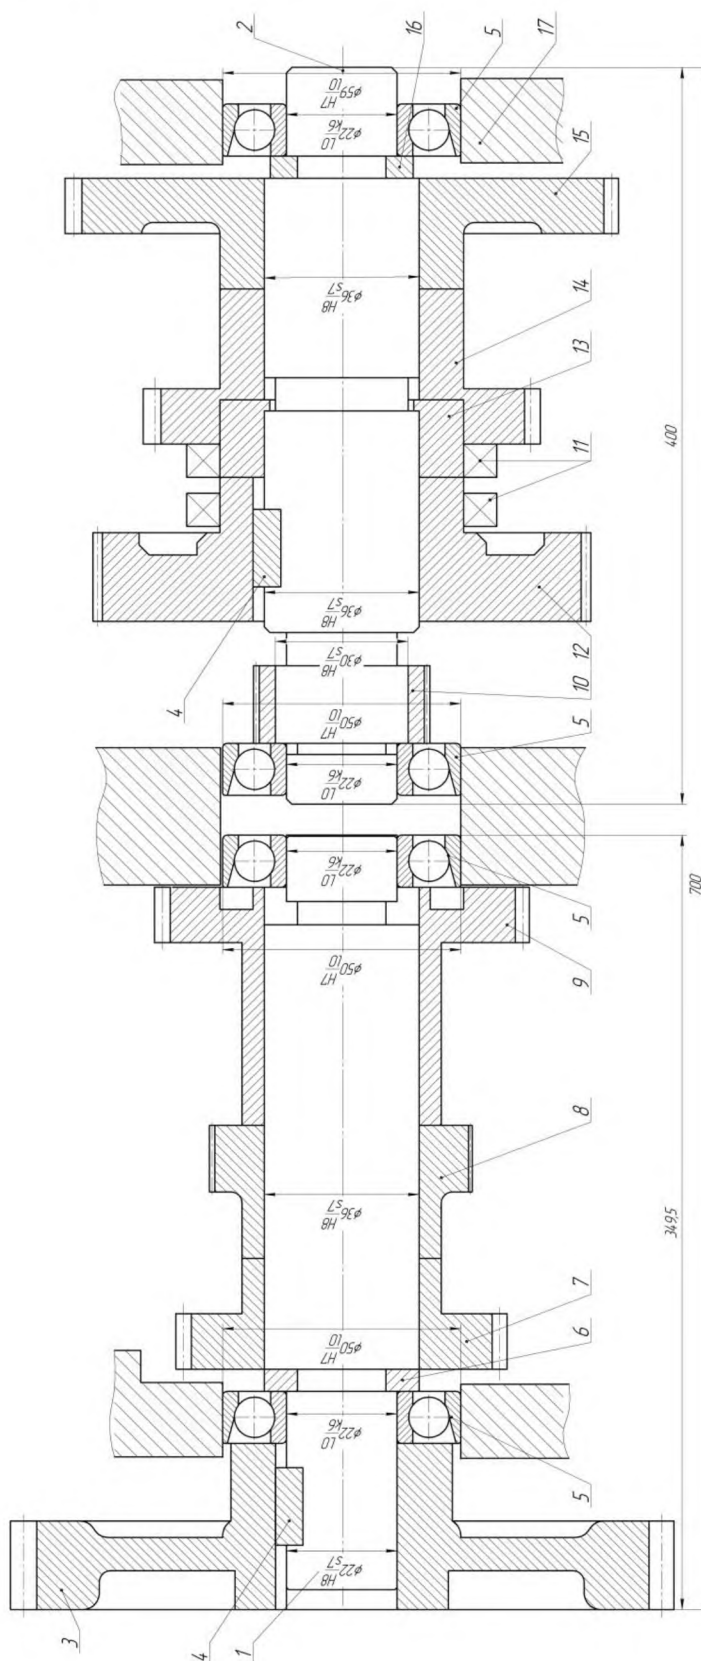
Вали коробки подач горизонтально-фрезерного верстата мод. 676
